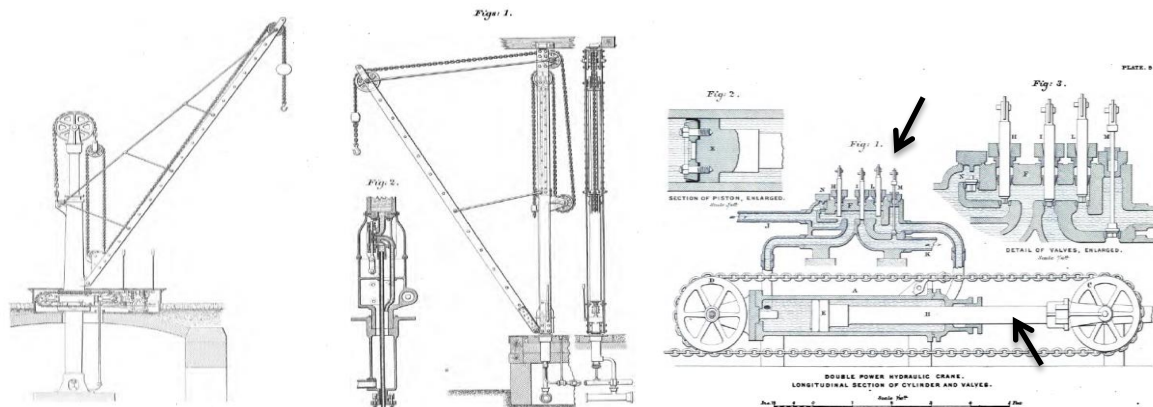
Titul Lit.17 Obr.178 Lití ingotu Obr.179 Titul Lit.13 Obr.180 Hydraulický manipulátor
